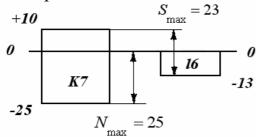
Схема расположения интервалов допусков при посадке подшипника в корпус
